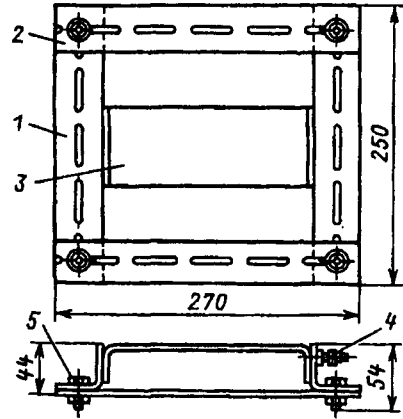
Рама для установки на стене: 1 — перфорированный уголок; 2 — перфорированная полоса; 3 — скоба; 4 — болт для заземления; 5 — детали крепления
